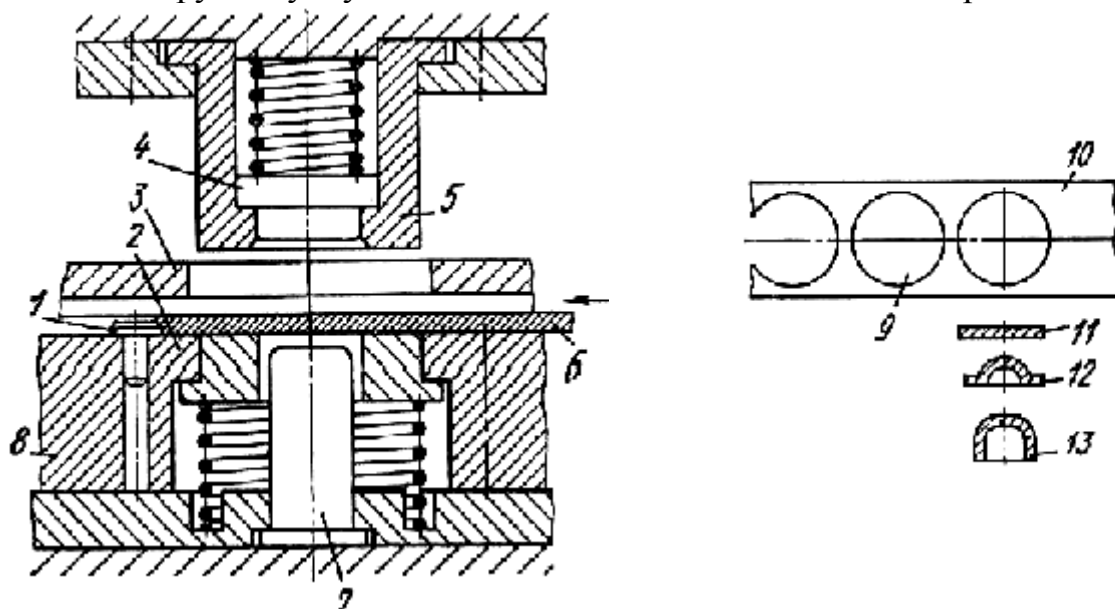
Схема штампа совмещенного действия для вырубки и вытяжки:
